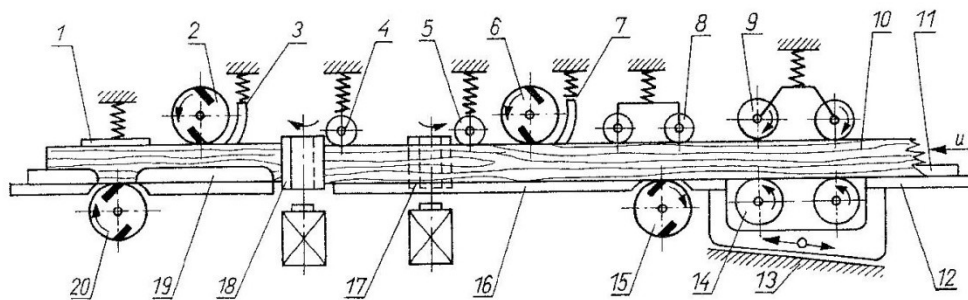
Strugarka trzystronna — widok ogólny [14]
